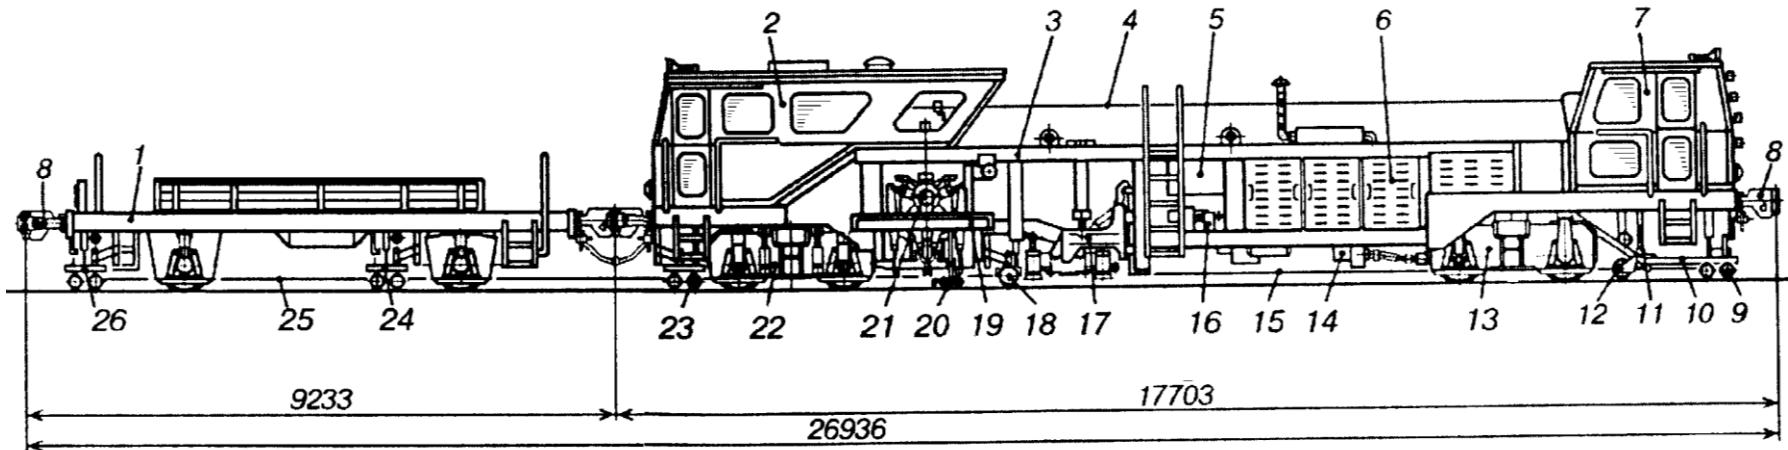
Выправочно-подбивочно-рихтовочная машина ВПР-1200: 1 – прицепная платформа; 2, 7 – кабины; 3 – рама; 4 – нивелировочные тросы; 5 – гидробак; 6 – силовая установка; 8 – автосцепки; 9, 18, 23, 24, 26 – тележки КИС; 10 – рычаг; 11 – штанги нивелировочных устройств; 12 – датчик пути; 13, 22 – тяговая и бегунковая тележки; 14 – силовая передача (трансмиссия); 15, 25 – трос-хорды КИС; 16 – насосная станция; 17 – ПРУ; 19 – уплотнители балласта; 20 – измерительное устройство нивелировочной КИС; 21 – подбивочные блоки
